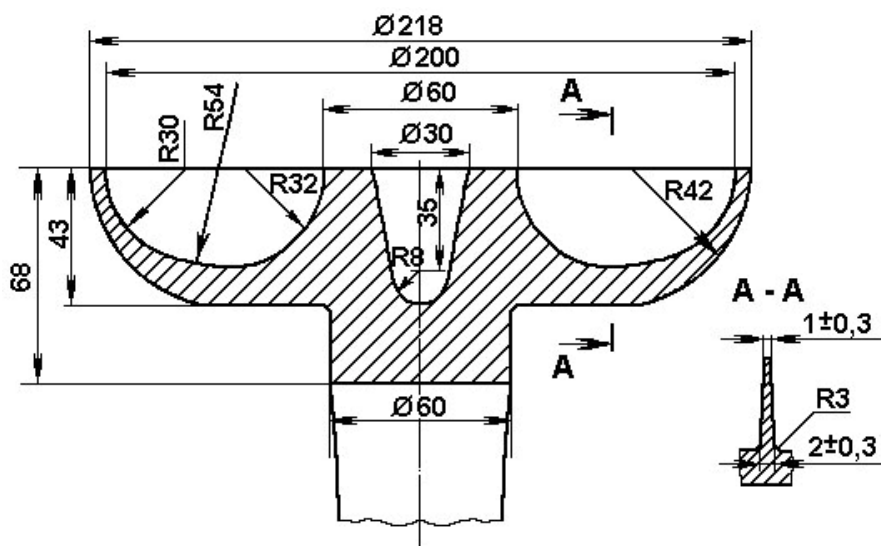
Чертеж отливки «Рабочее колесо гидромолоты»
